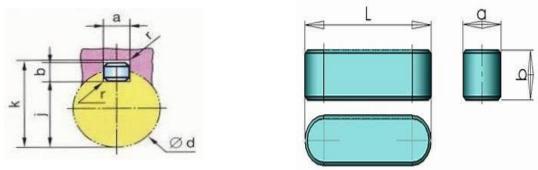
DESSIN CLAVETTE ET SURFACE CISAILLER
